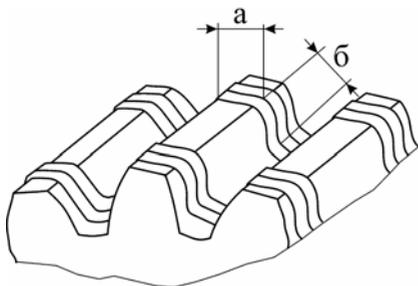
Схема прокатывания пластинки или проволоочки
